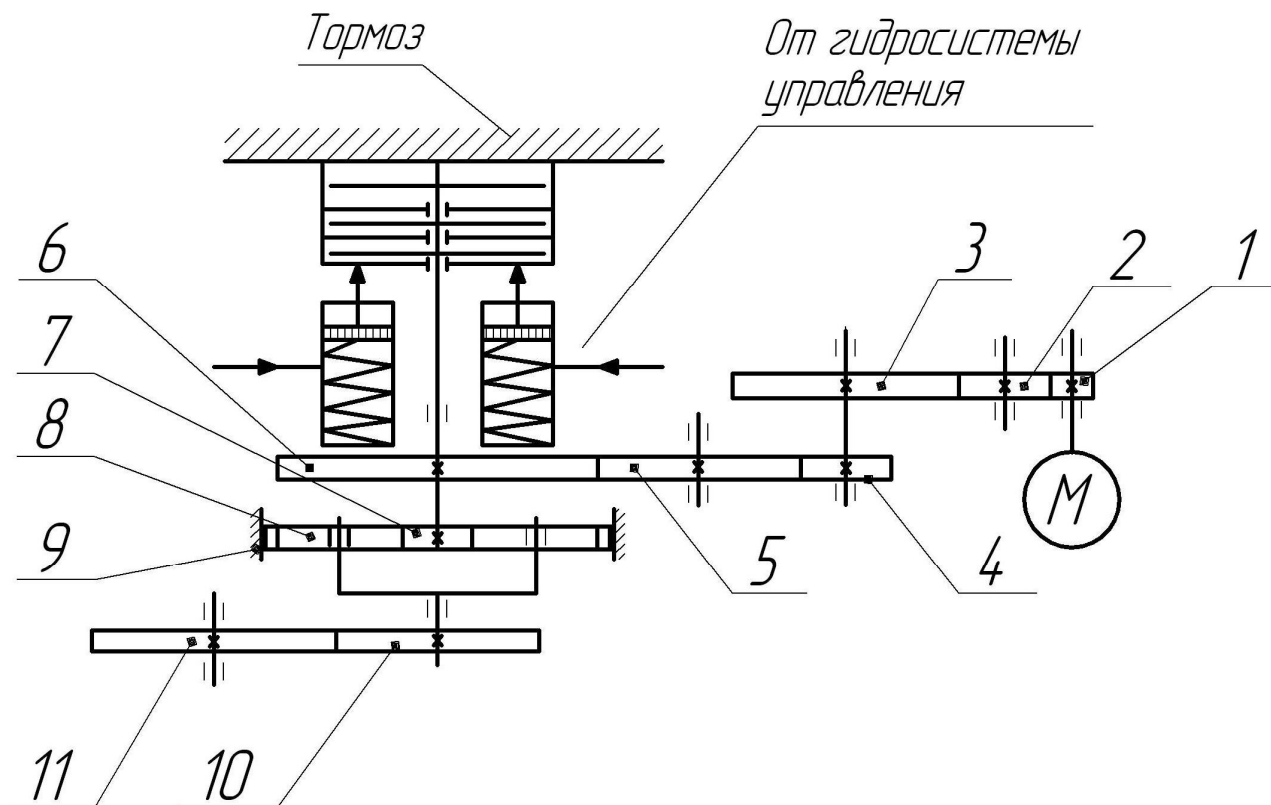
Кинематическая схема редуктора механизма подачи
